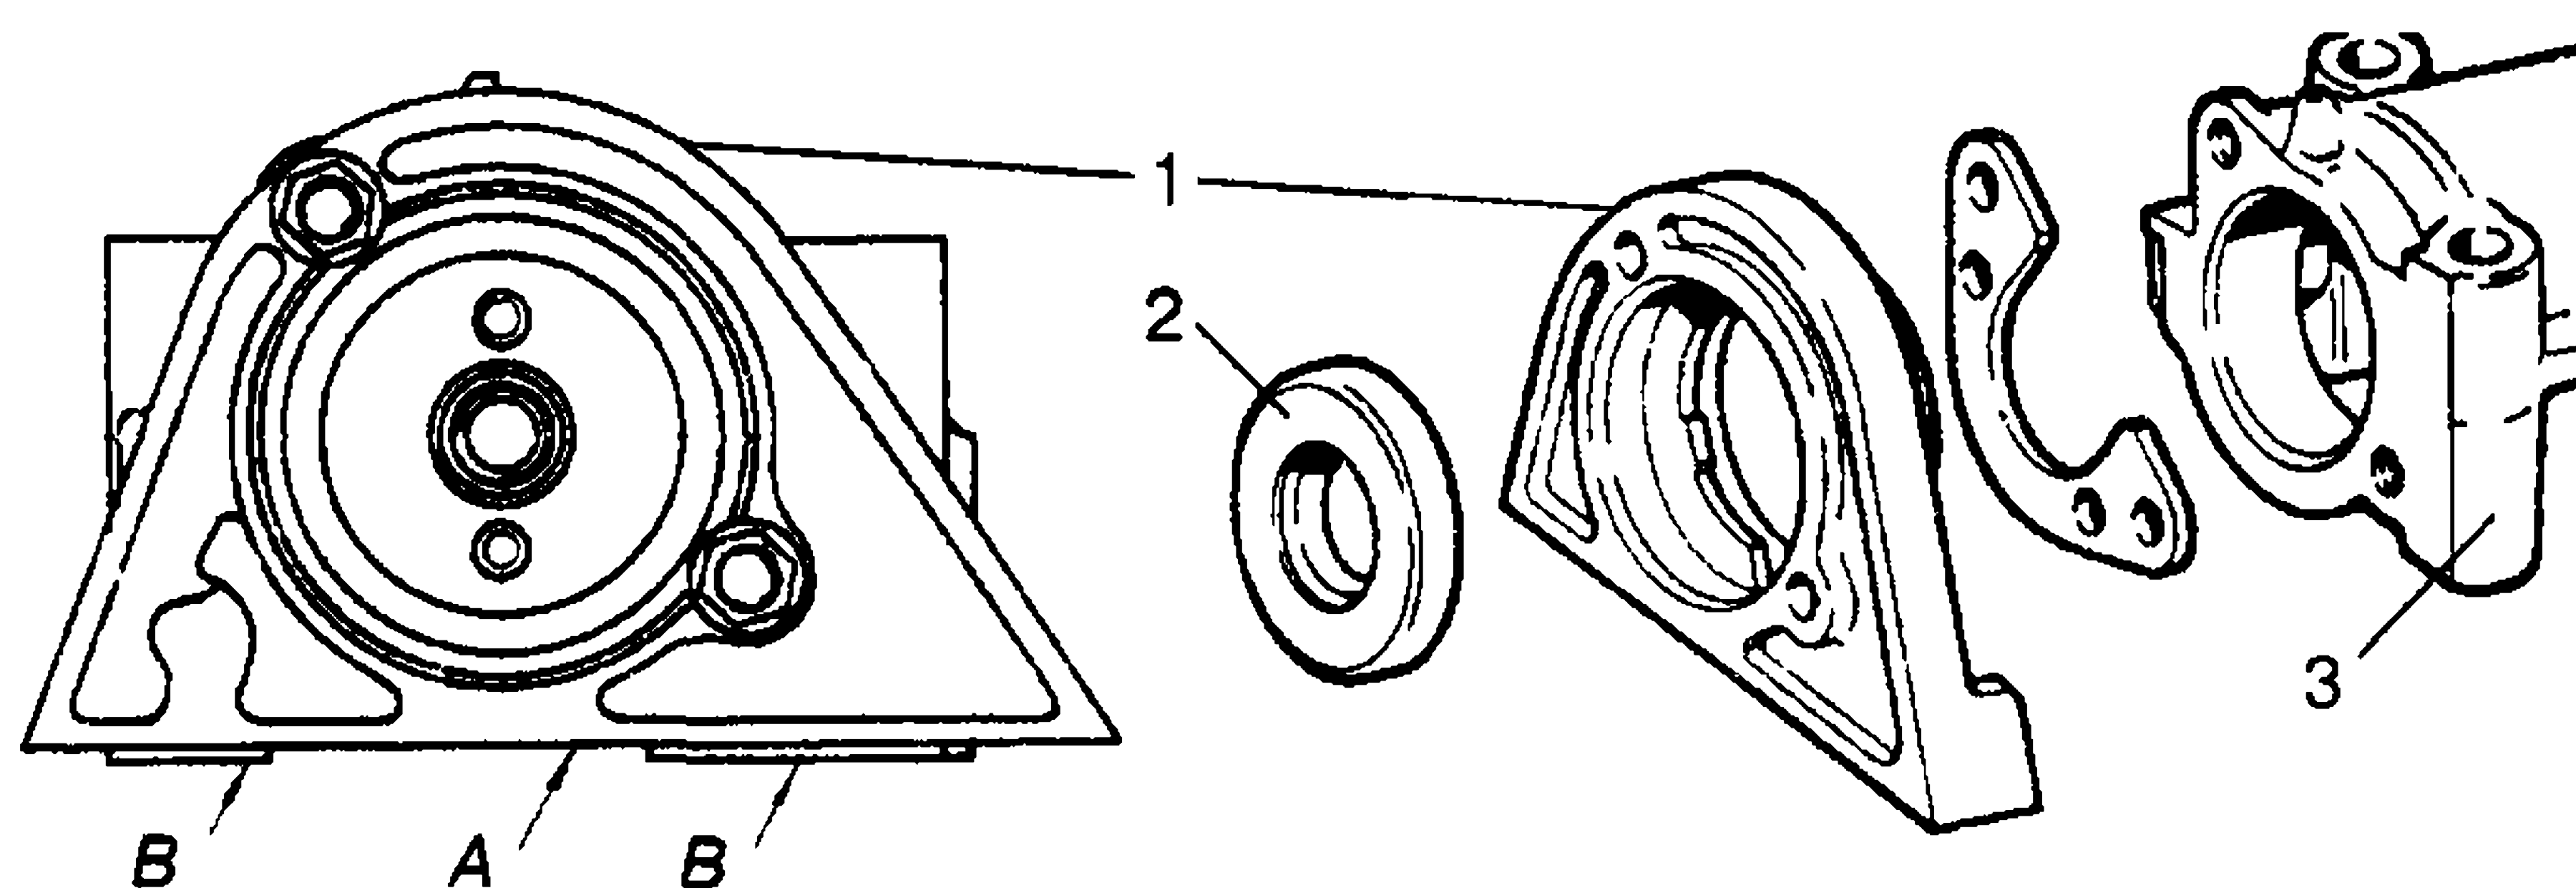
Держатель сальника и сальник распредвала двигателя 2105:
